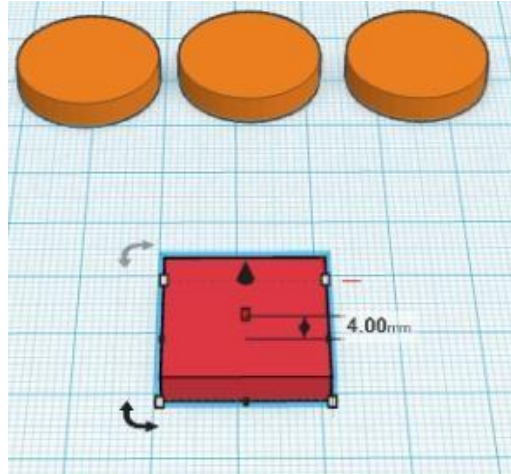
OBJET BOÎTE REDIMENSIONNÉE SUR LE PLAN DE TRAVAIL
